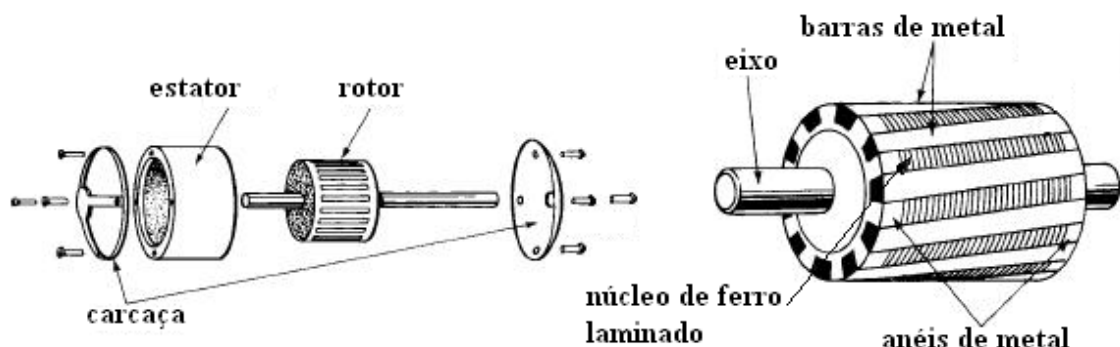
Forma construtiva do Motor de Indução. Vista explodida e rotor em detalhe.
